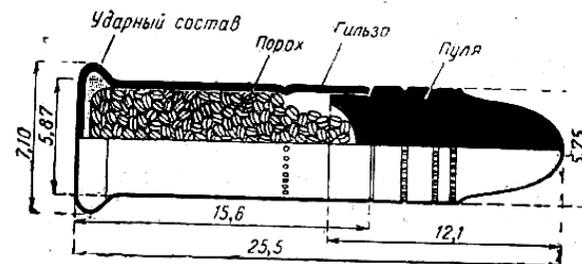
5,6-мм малокалиберный патрон (длинный винтовочный).
